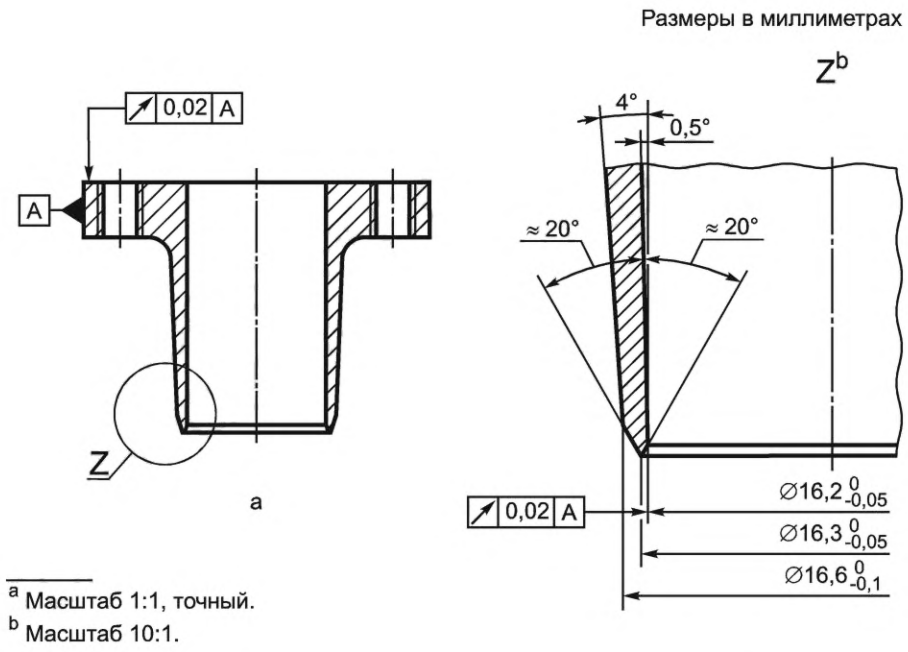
Полое сверло для подготовки испытуемого образца
